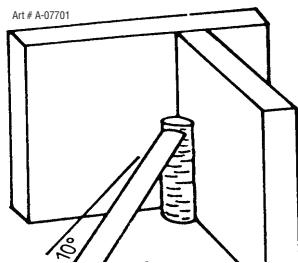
Soudure d'angle verticale à un seul passage
